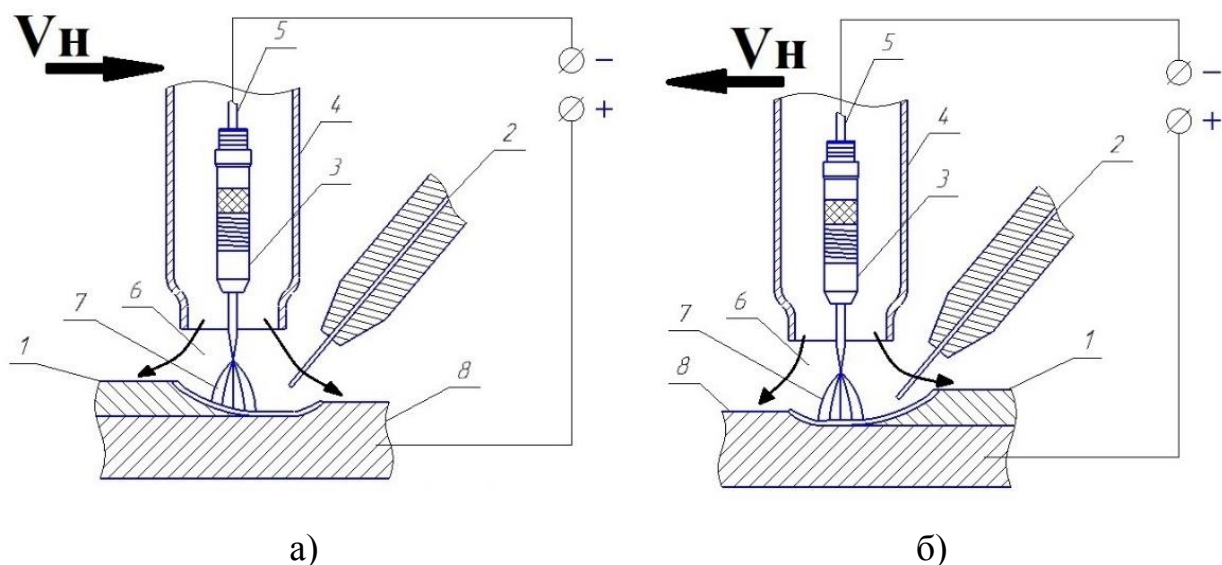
Схема процесса аргодуговой наплавки неплавящимся электродом: а) левый способ наплавки (проволока подается в головную часть сварочной ванны) б) правый способ наплавки (проволока подается в хвостовую часть сварочной ванны)
